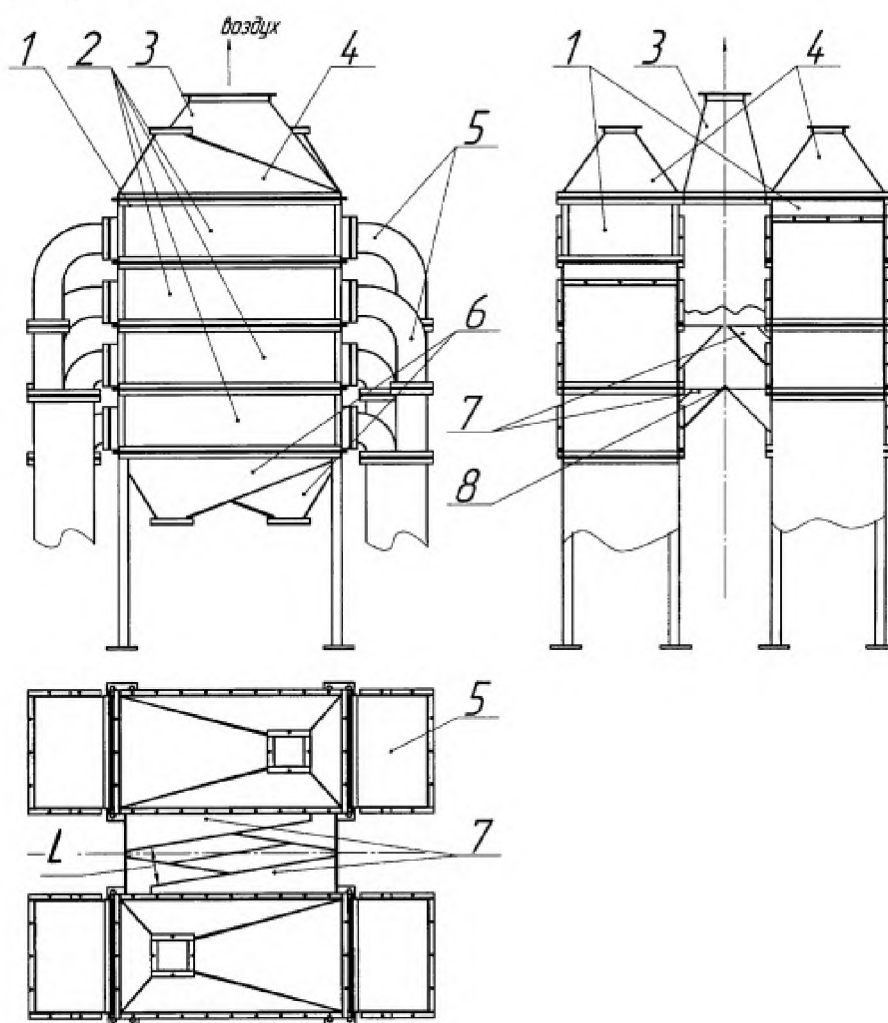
Принципова схема аерожолобної шахтної сушарки: 1 – шахти; 2 – повітророзподільні коробки; 3 – конфузор; 4 – надсушильний бункер; 5 – аеродинамічні коробки; 6 – підсушильний бункер; 7 – кармани; 8 – козирки; 9 – перегородки
